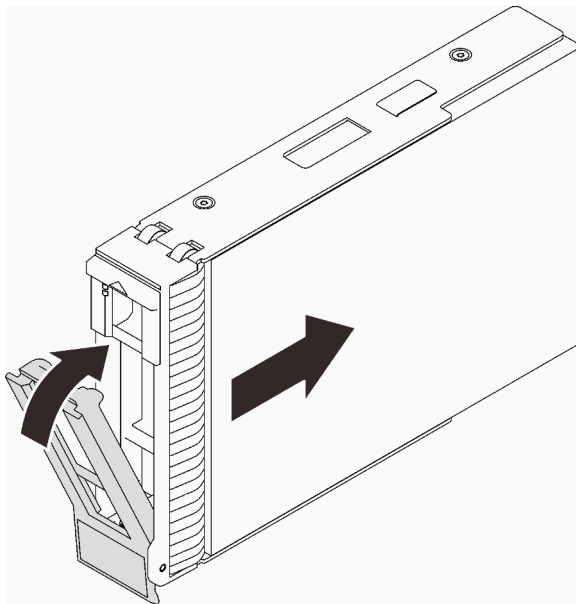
Installieren des Hot-Swap-Laufwerks
